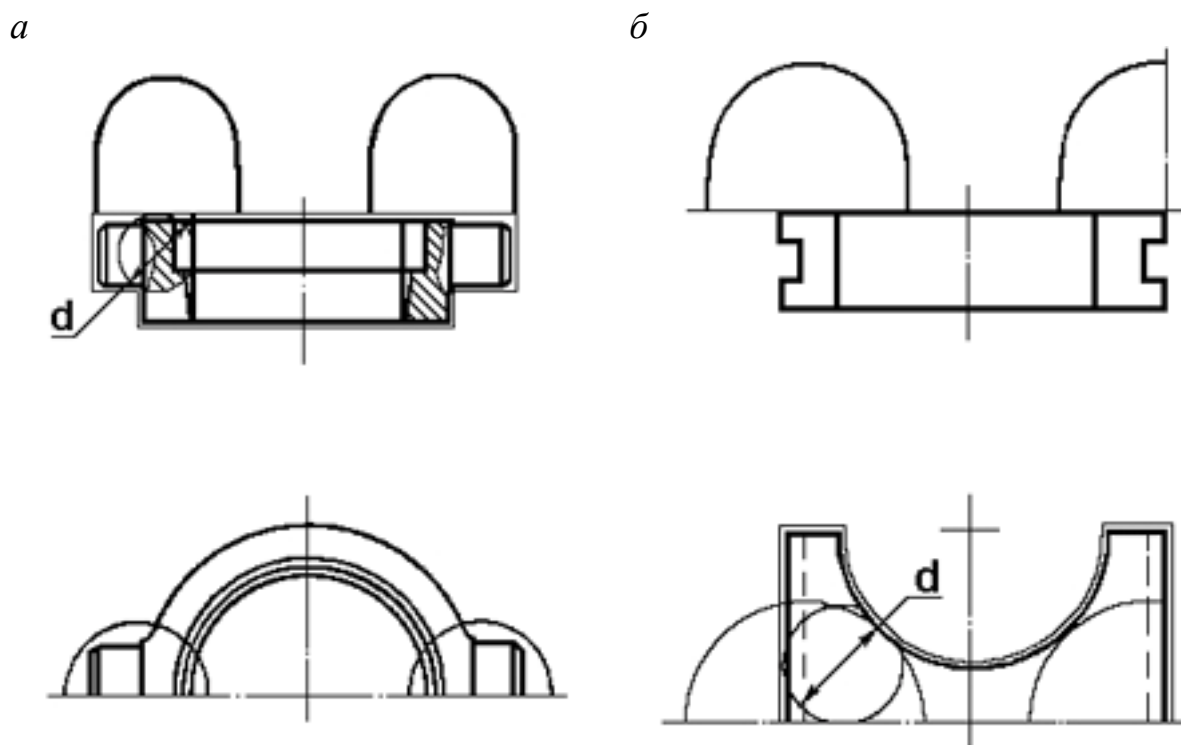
Схемы установки прибылей на узлах отливки:
